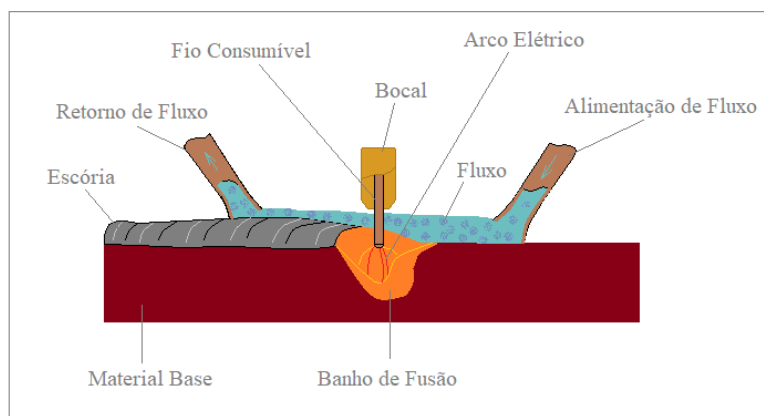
Soldadura por arco submerso, SAW – [10] Imagem adaptada
